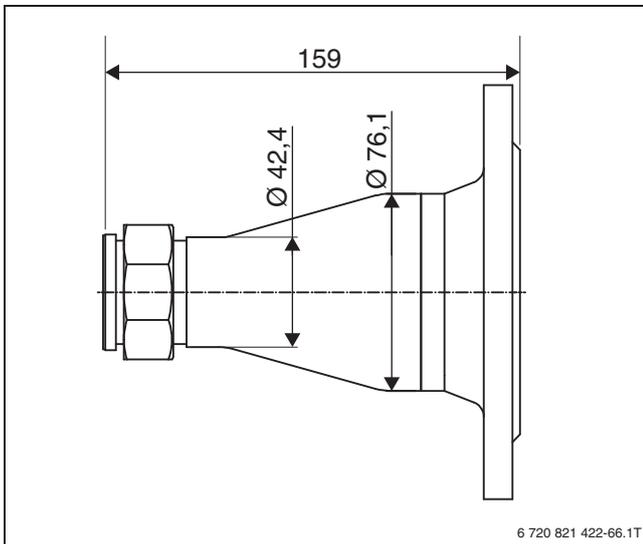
Übergangsstück DN 65/PN 6 – G 1 ½ " (Maße in mm)
